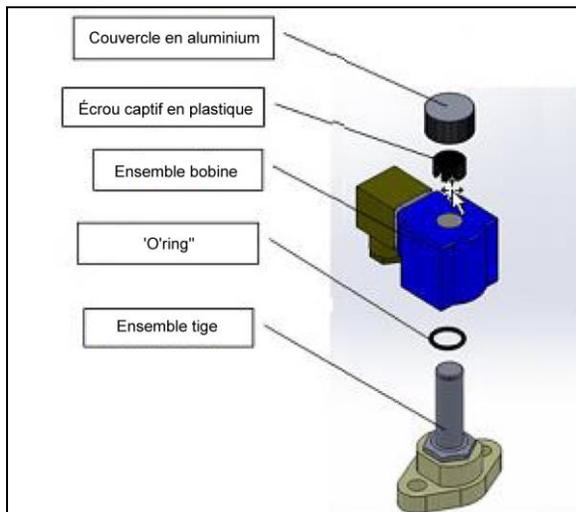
BOBINE DE LA SOUPE DE DÉLESTAGE
